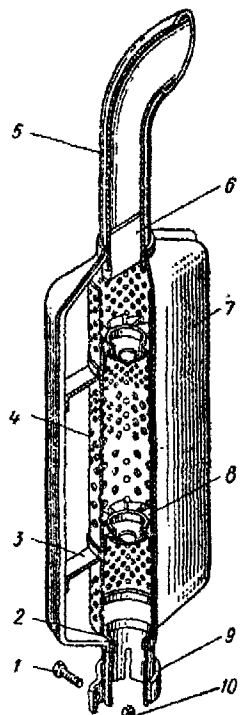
Глушитель: 1 – болт; 2 – патрубок; 3 – перегородка; 4 – труба резонатора; 5 – трубопровод; 6 – пластина; 7 – корпус; 8 – завихритель; 9 – хомут; 10 – гайка
